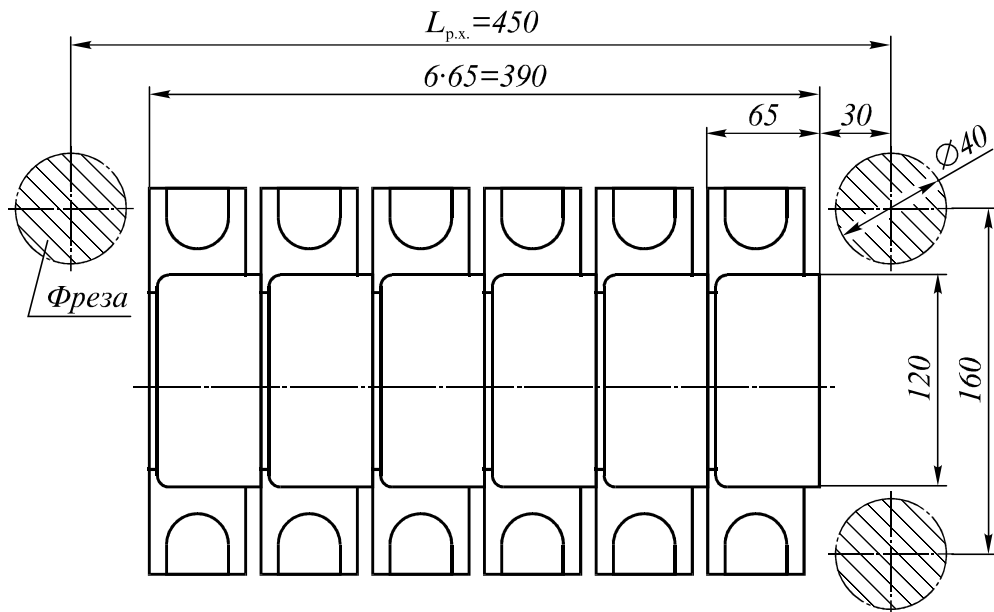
Схема обработки заготовок в приспособлении
